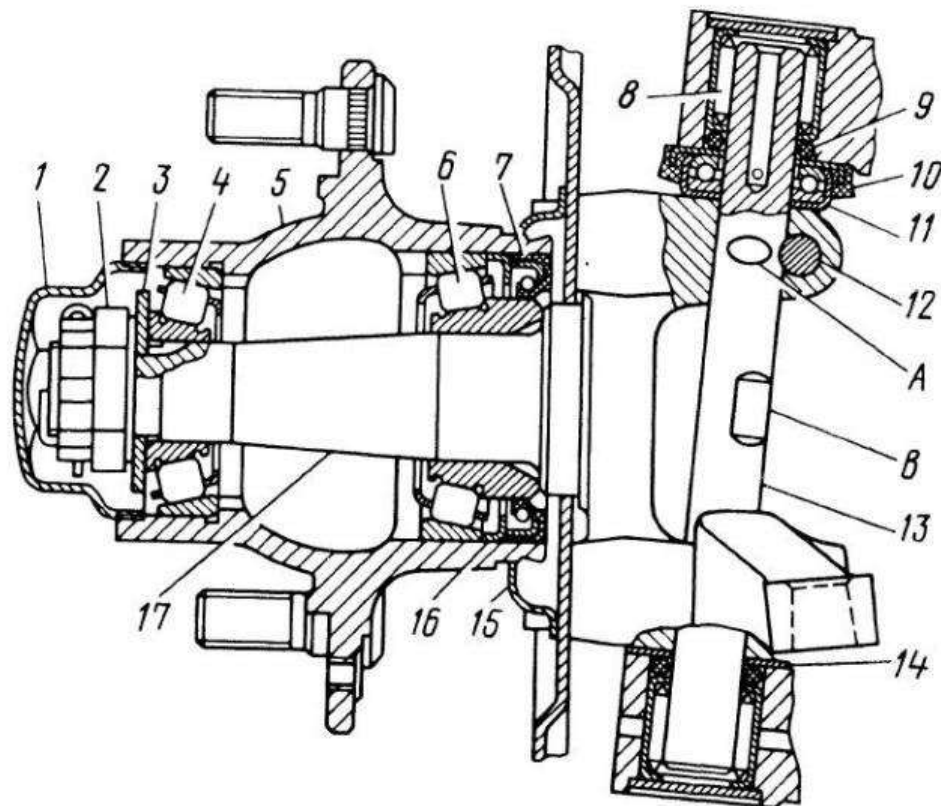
Поворотний кулак і маточина переднього колеса:
